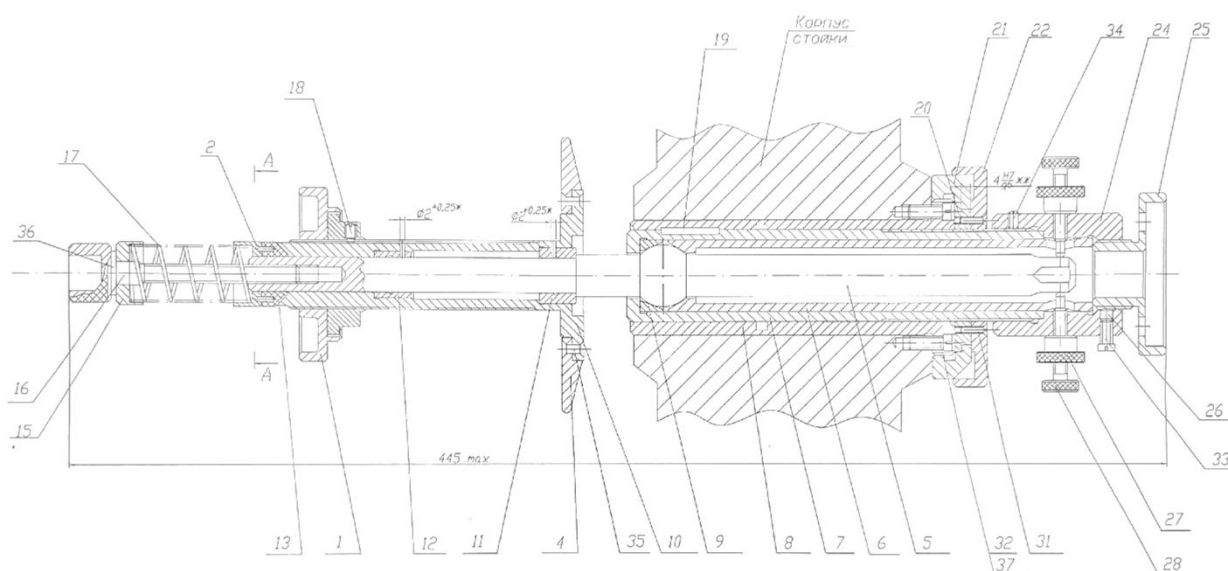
Механизм ременного редуктора (компоновочный чертеж)
